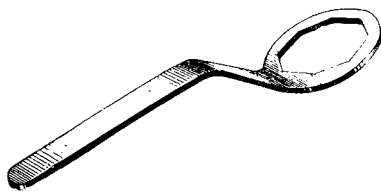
Ключ накидной 47001-1-010МД для гайки дет. 233-12-168 коробки передач
